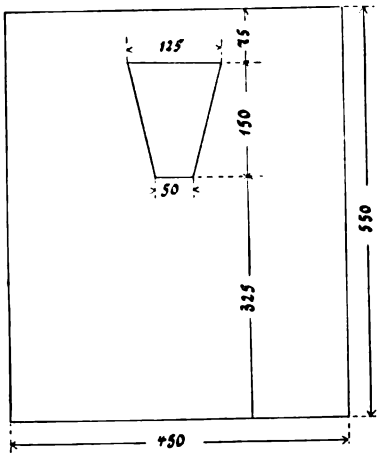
Vorderansicht des Wasserkastens. Die Zahlen geben die Länge in Millimeter an.
